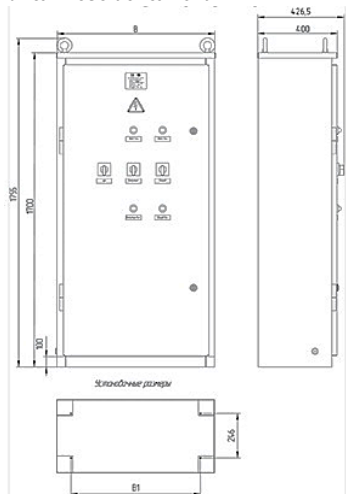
Общий вид и габаритные размеры ШСН навесного исполнения
